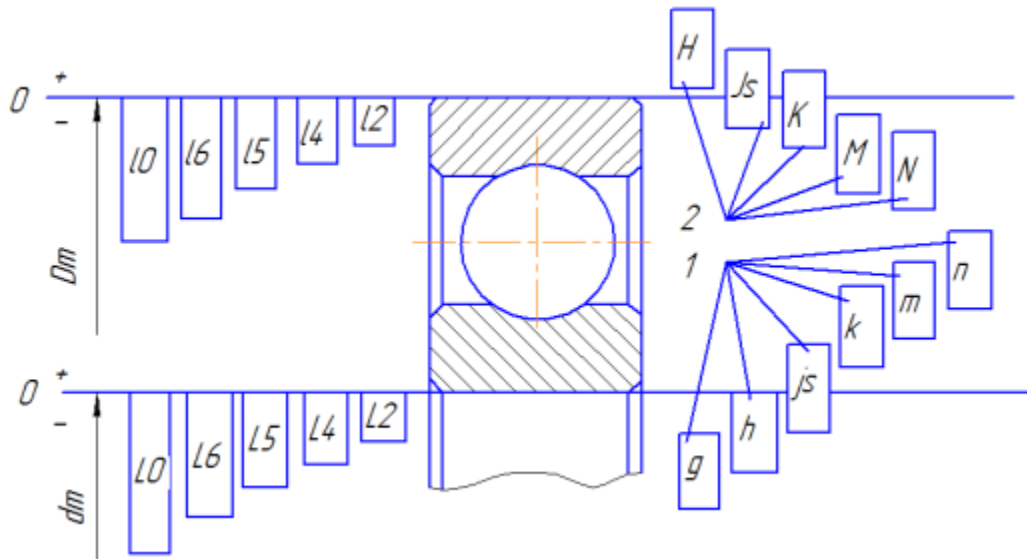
Схема розташування полів допусків на діаметри кілець підшипників і сполучених з ними валів (1) і корпусів (2)
